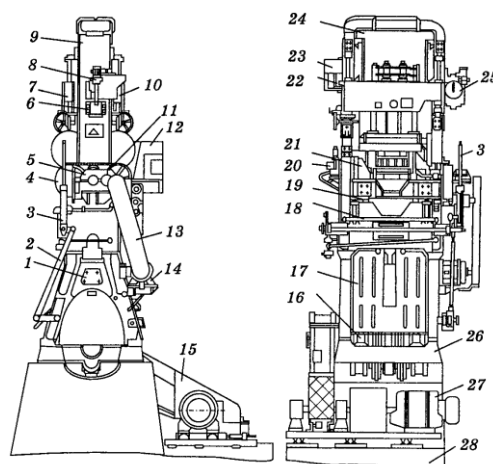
Загальний вигляд двоповерхової пилорами: 1 – стійка; 2 – гальмо; 3 – важіль гальма; 4 – огороження вальців; 5 – редуктор механізму подачі; 6 – механізм приводу верхніх вальців; 7, 10 – верхні передні та задні ворота; 8 – механізм зміни нахилу пилкової рамки; 9 – остов станини; 11 – нижній задній валець; 12 – напрямний апарат; 13 – огороження приводу подачі; 14 – привод механізму подачі; 15 – огороження приводу механізму різання; 16 – кривошипно-повзунний механізм; 17 – лоток для тирси; 18 – система охолодження; 19 – пилкова рамка; 20 – мастильна система; 21 – нижні передні ворота; 22 – механізм зміни швидкості подачі; 23 – огороження механізму зміни подачі; 24 – огороження пилкової рамки; 25 – показник швидкості подачі; 26 – фундаментна плита; 27 – головний привод; 28 – фундамент
